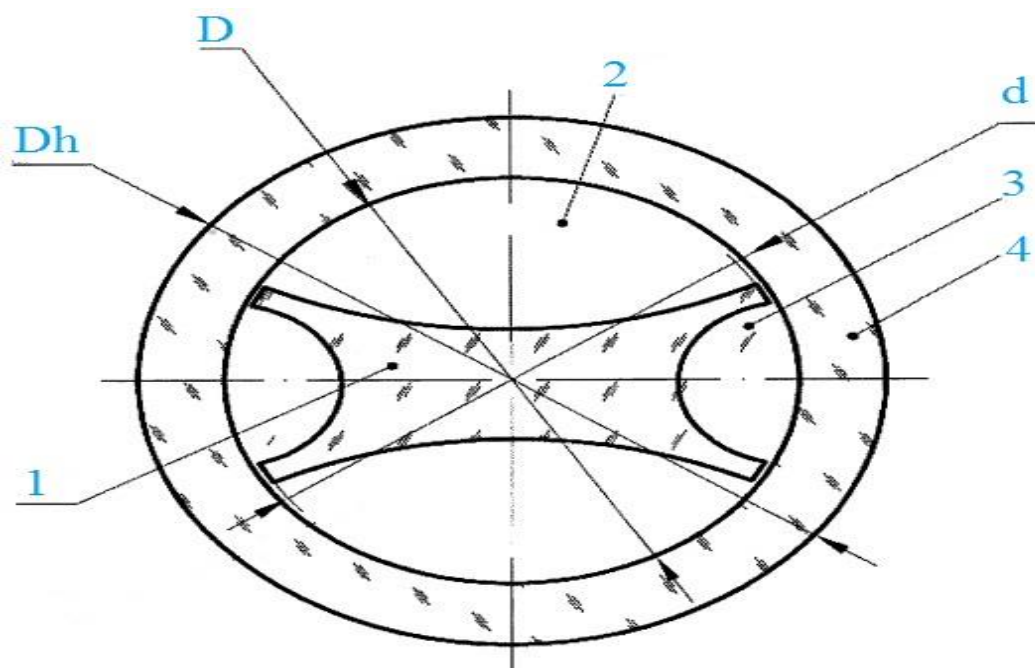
Схема расположения и формы пазов на заготовке сердцевины
